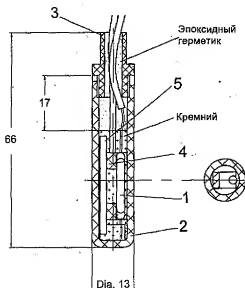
б. Поворотная часть конструкции реле типа RG-25: 1 — геркон; 2 — изолятор; 3 — втулка; 4 — опора; 5 — ферромагнитная пластина
